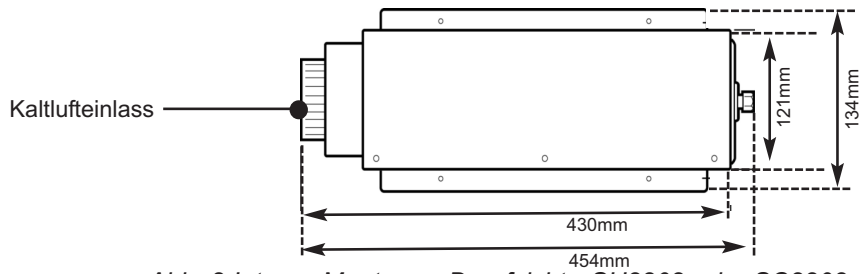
Interne Montage - Draufsicht - SH2202 oder SC2202
